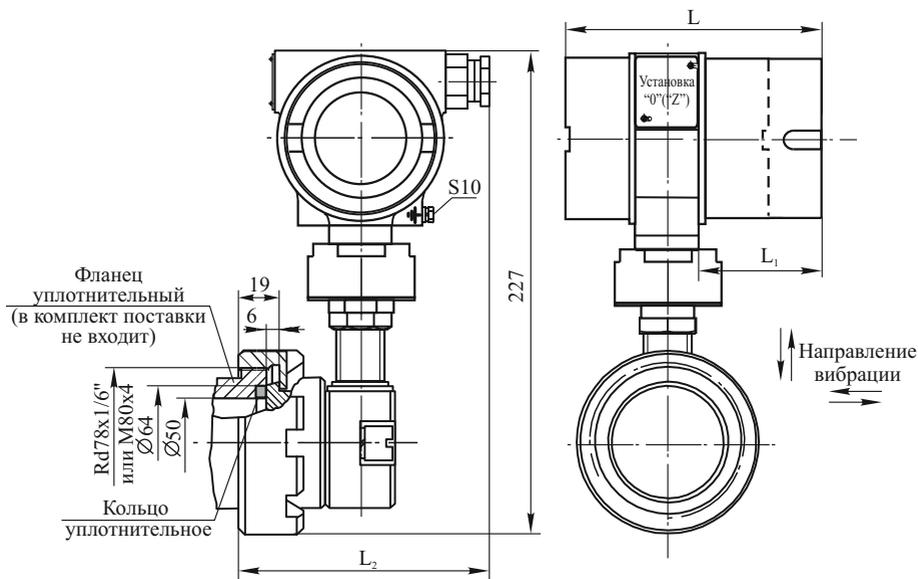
а - Установка монтажных деталей для крепления на трубе.
